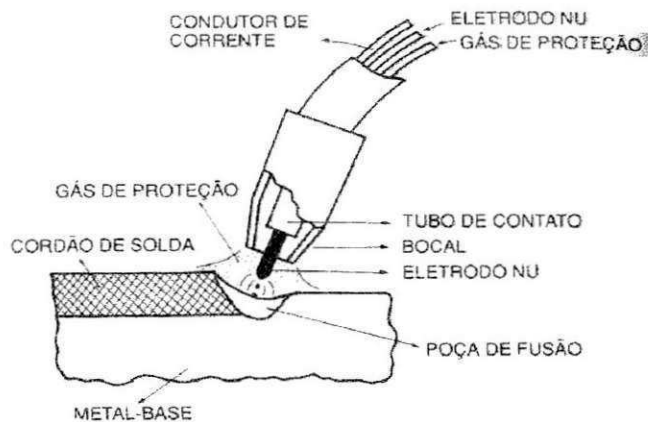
Esquema básico do processo de soldagem MIG/MAG.
